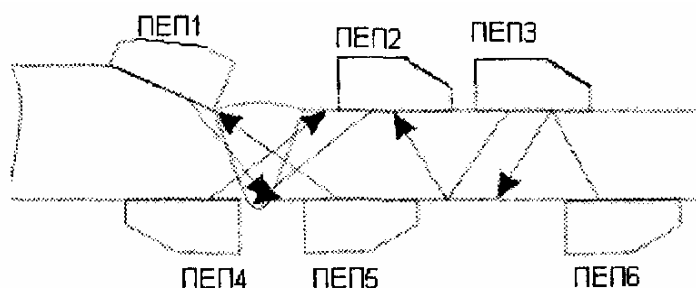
Схема контроля сварного соединения с разной толщиной сваренных элементов
